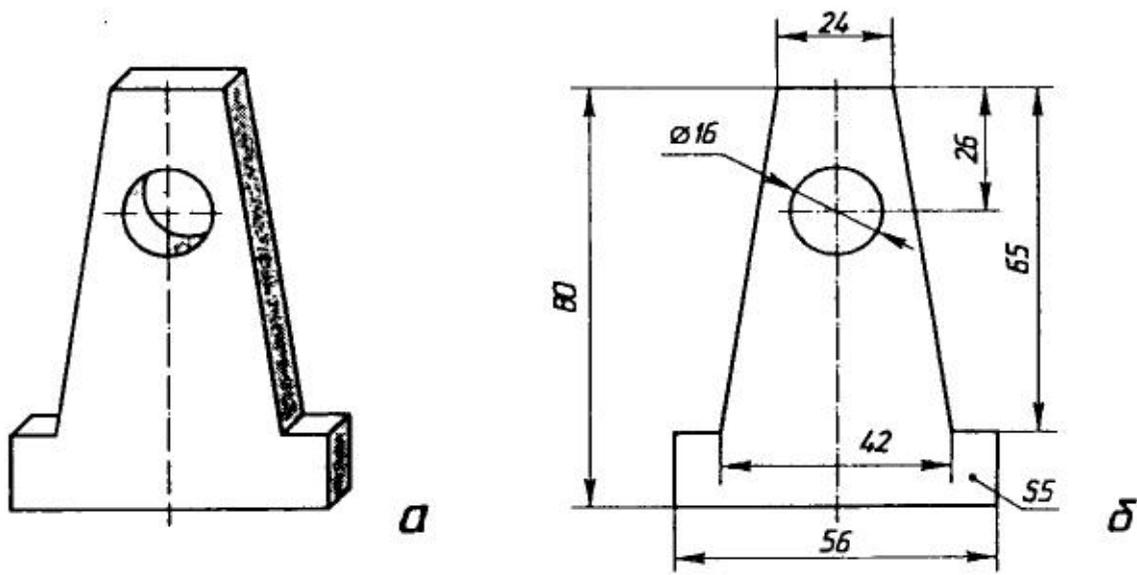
Зображення плоскої деталі: *a* — загальний вигляд; *б* — креслення.
